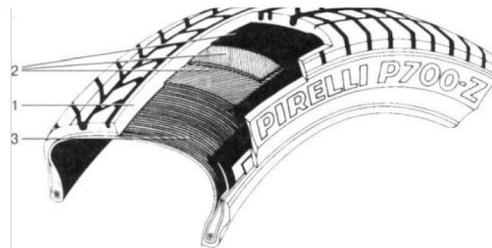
Конструкция радиальной металлокордной шины: 1-протектор; 2-брекер из нескольких слоев нейлоновой ткани (сверху) и металлокорда (снизу); 3-радиальные нити металлокордного каркаса.
